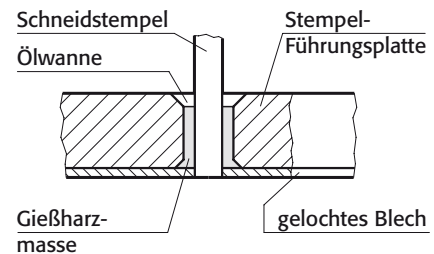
Vergossener Schneidstempel für schnelllaufende Werkzeuge.
